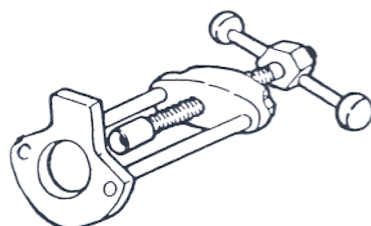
A-19B-01 — Extractor e insertador rodamiento eje auxiliar Tr/D 66608-AB
